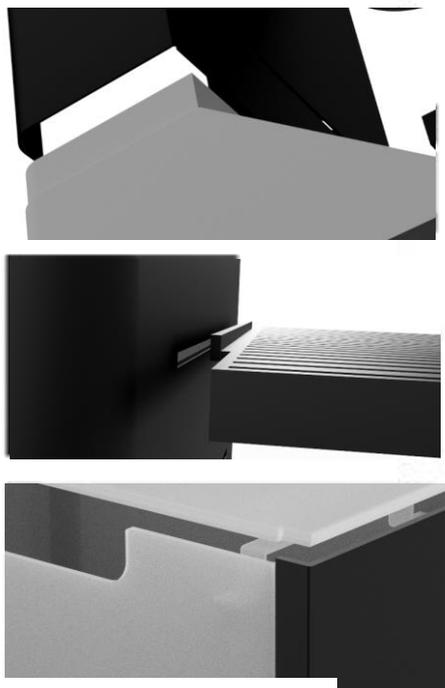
Vistas, explosionado y detalles de la primera alternativa
